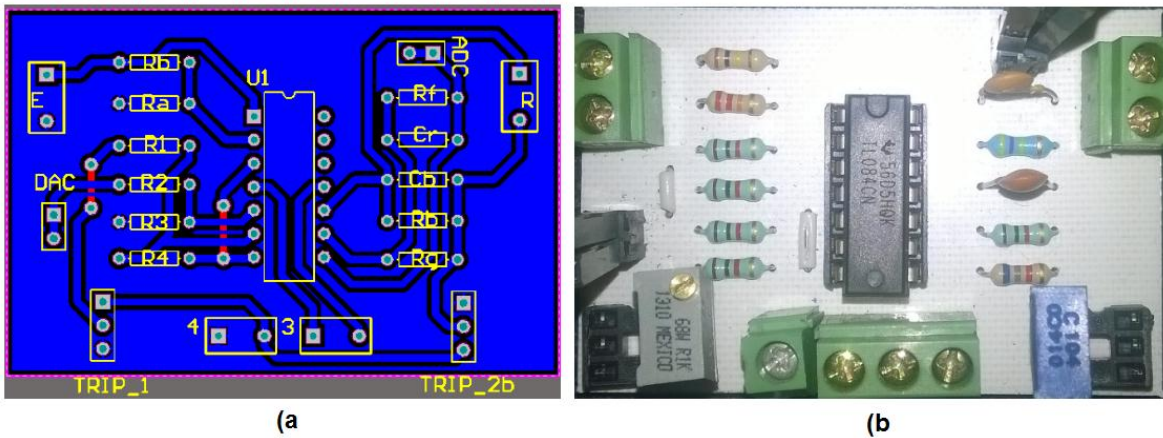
(a) Diseño de tarjeta para acondicionamiento de señales. (b) PCB construida de la tarjeta para etapa de acondicionamiento.
